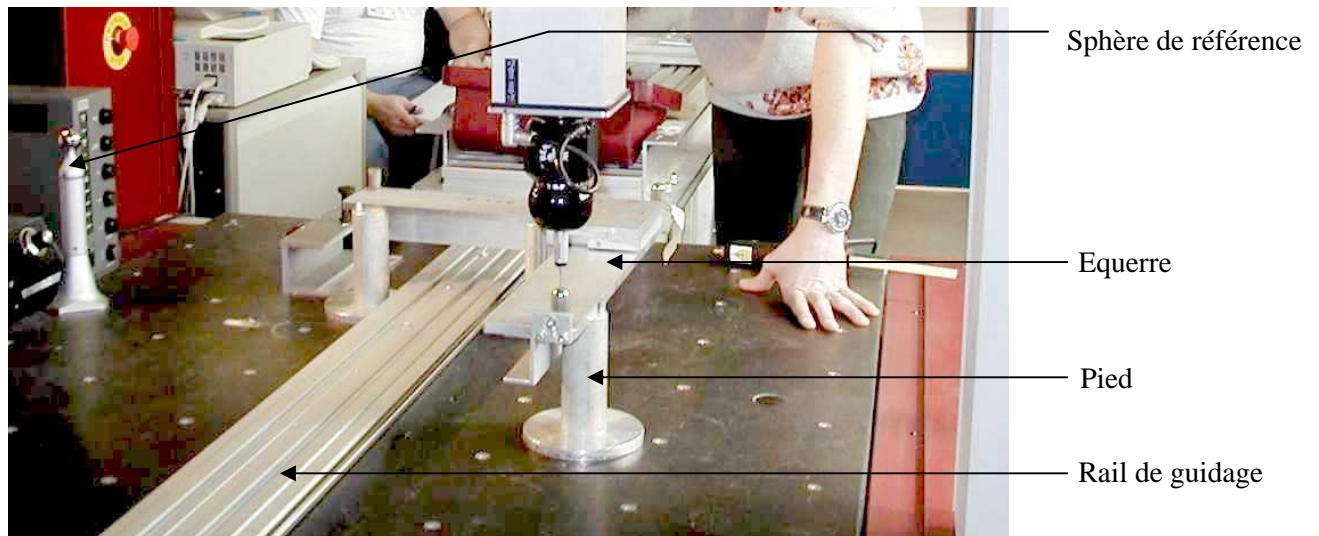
réglage d'une équerre sur la machine tridimensionnelle du LAL d'Orsay.
